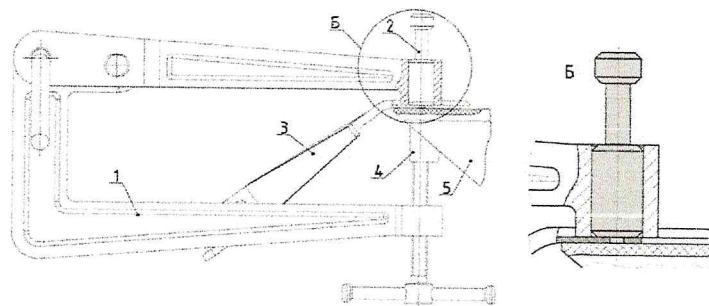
Разрез кондукторной скобы, выполненной по второму варианту
